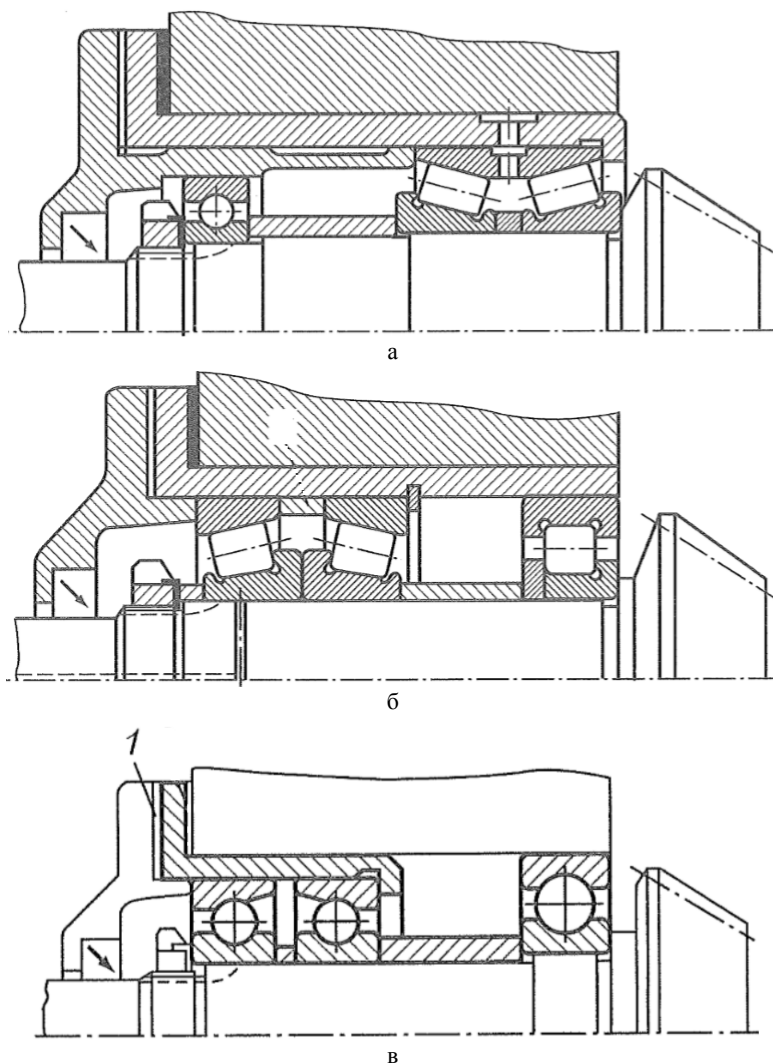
Варианты конструкций подшипниковых узлов с одной плавающей и одной фиксирующей опорой для конического вала-шестерни
